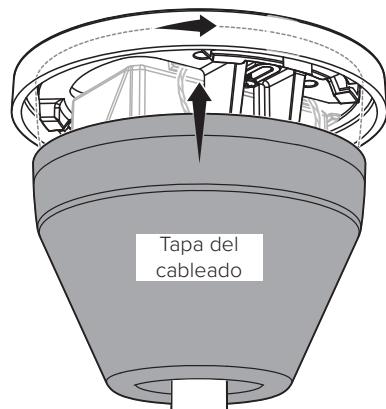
ventiladores con cubierta para el soporte de montaje
